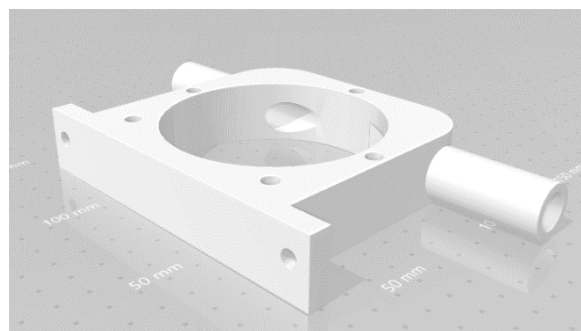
Disposició de la peça 1 del cos principal per ser impresa
